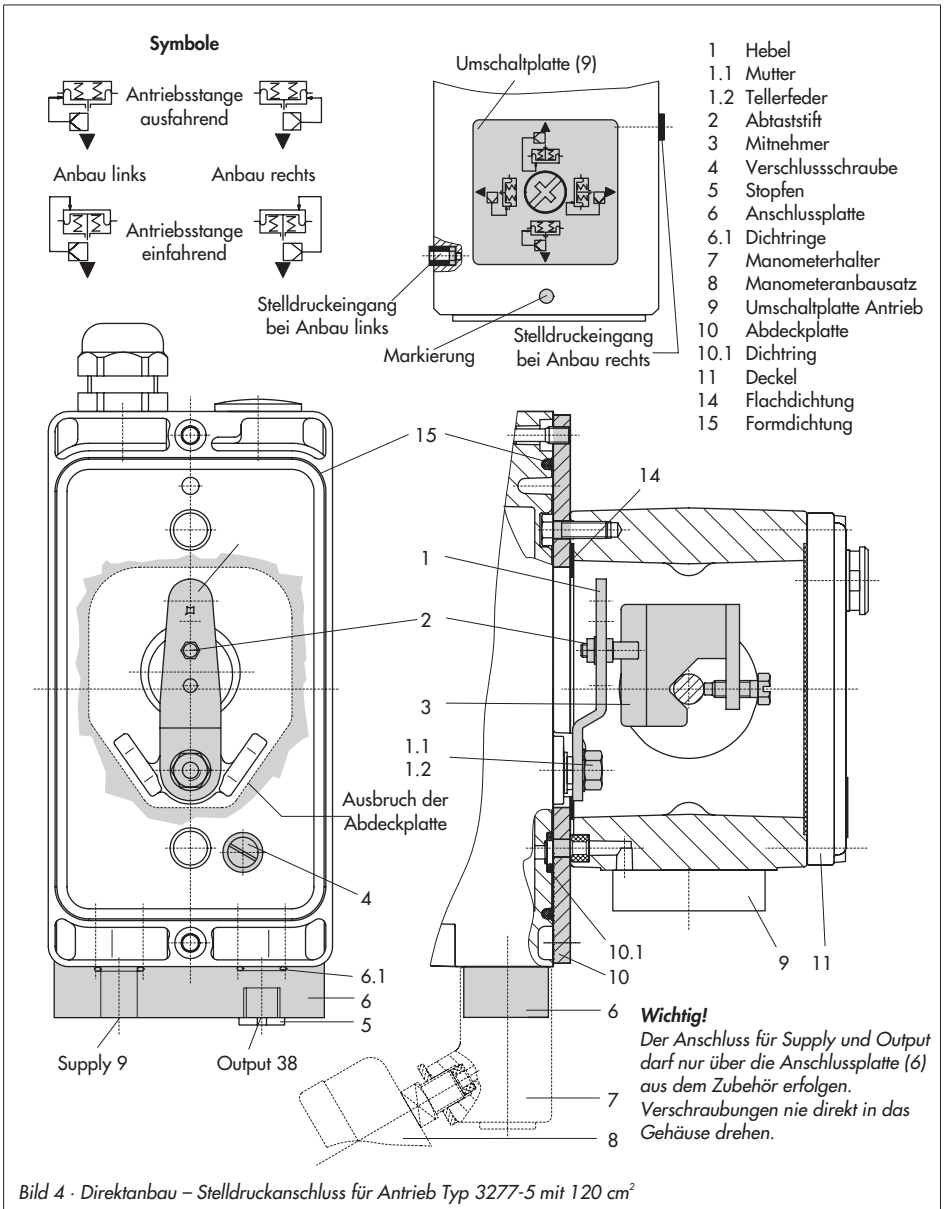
· Direktanbau – Stelldruckanschluss für Antrieb Typ 3277-5 mit 120 cm²
